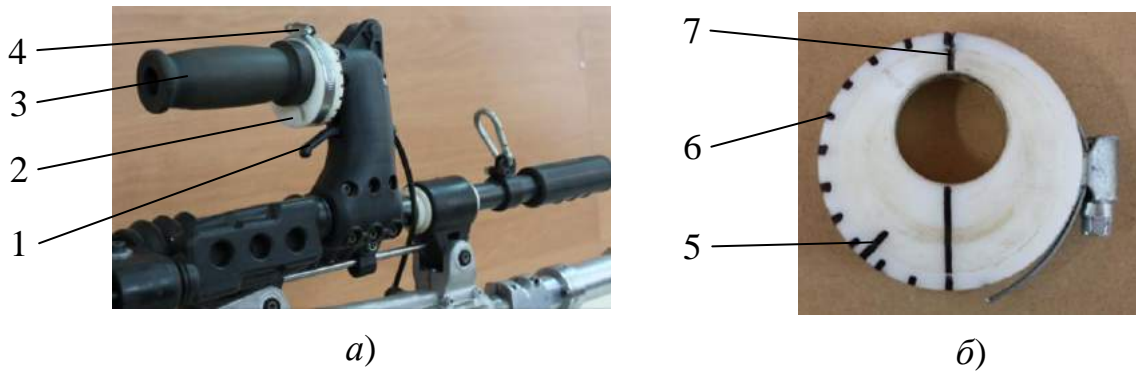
Дисковий обмежувач подачі палива (*а* – кріплення на задній рукоятці струшувача; *б* – вигляд зверху): 1 – важілець управління системою подачі палива; 2 – дисковий обмежувач; 3 – рукоятка; 4 – затискний хомут; 5, 6 і 7 – поділки відповідно вступання в дію обгінної муфти збурювача коливань, проміжної і максимальної подачі палива
